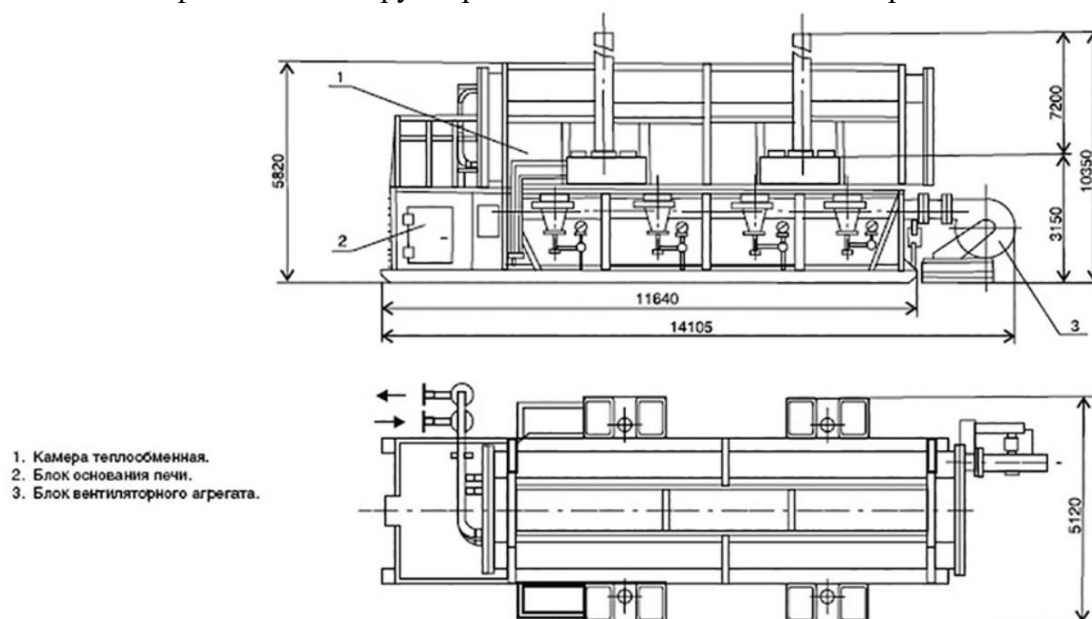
Конструкция печи трубчатой блочной (ПТБ-10) [1]
